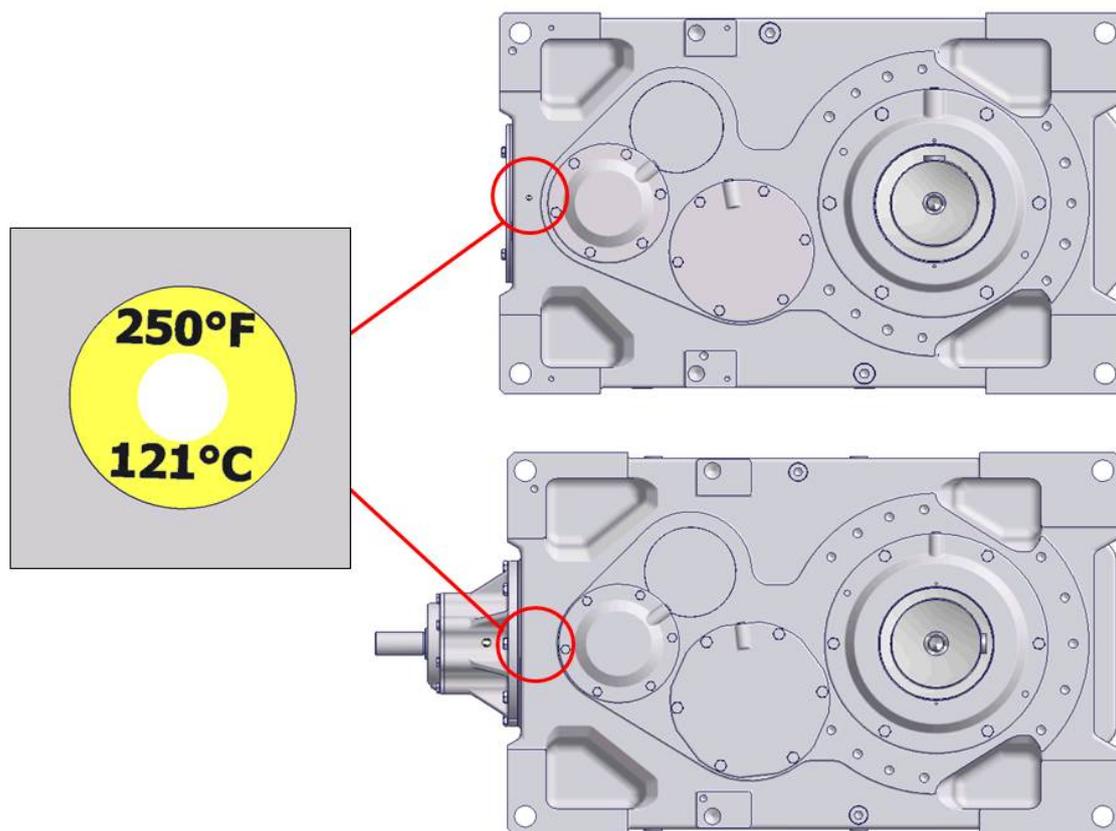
Position de la pastille de température sur le réducteur à engrenages cylindriques et couple conique
